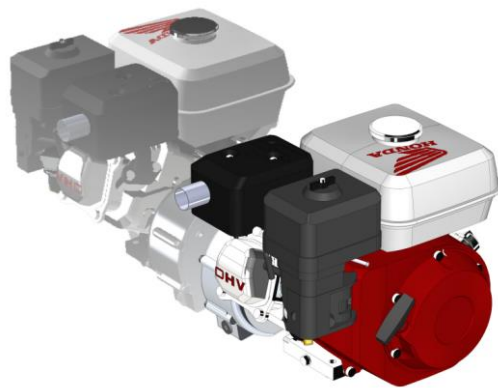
Diseño del motor en SolidWorks del Iron horse.
